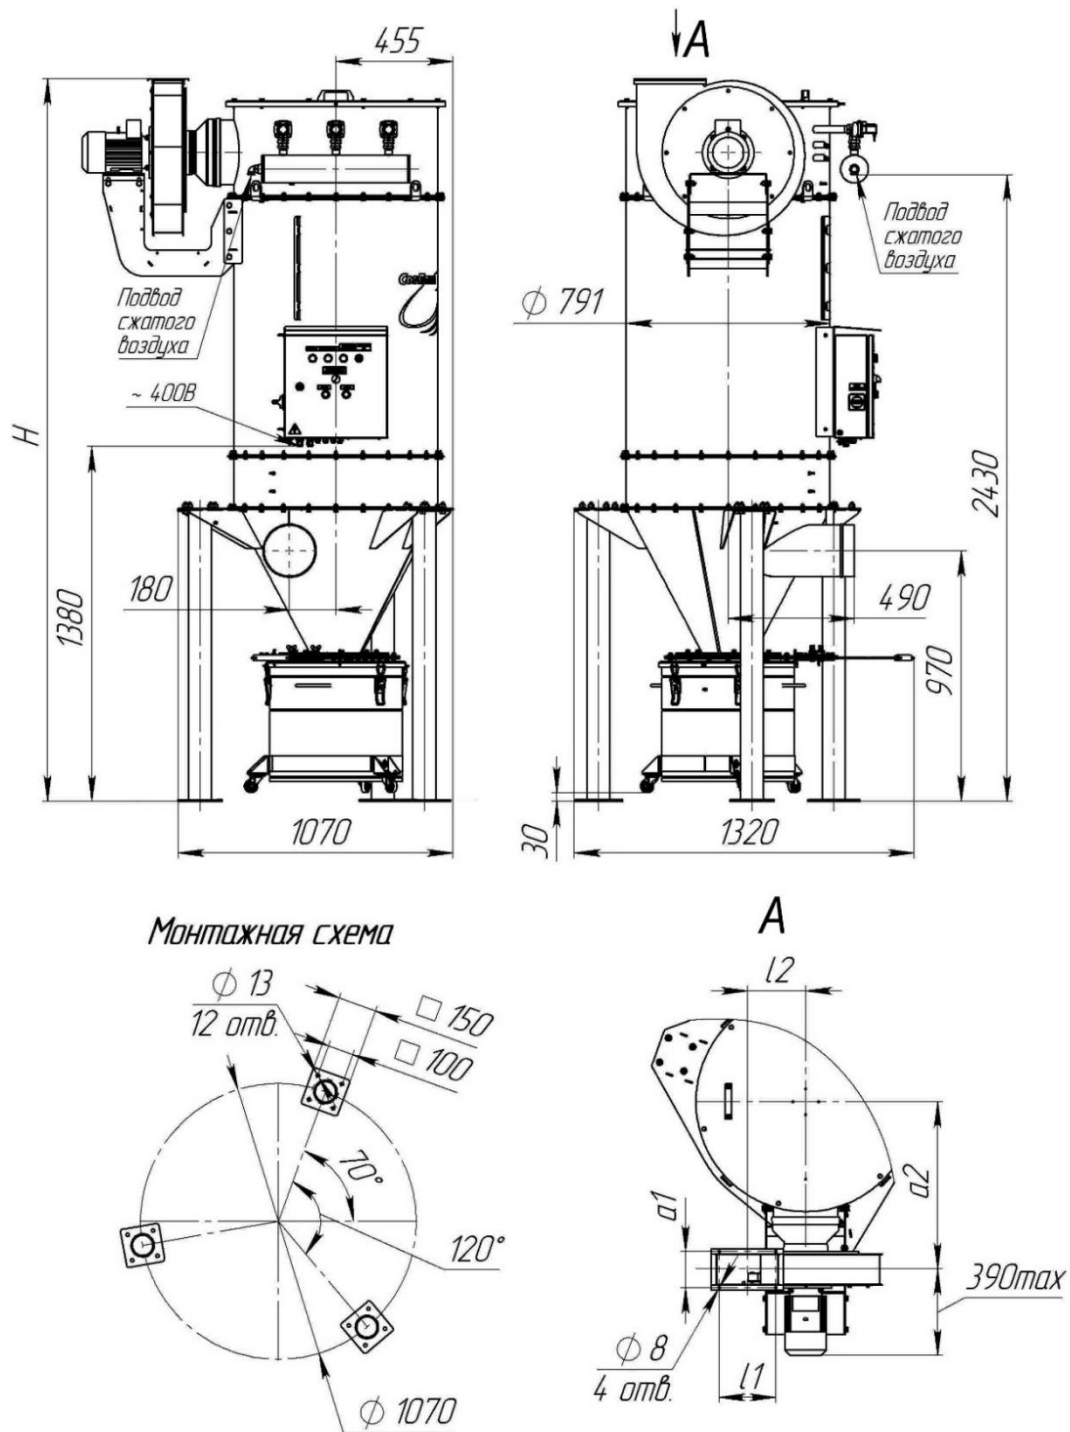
Габаритные и присоединительные размеры фильтров SFB-27-GV/DB-... с вентилятором
